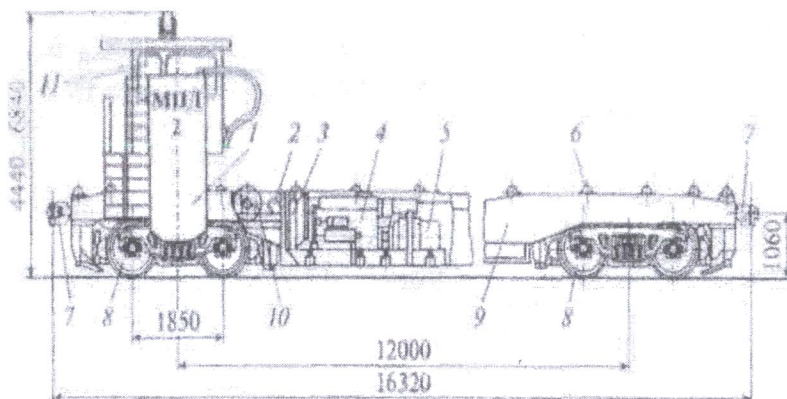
Моторная платформа МПД-2: 1 - порталная стойка с гидроцилиндрами вертикального перемещения кабины управления; 2 - компрессор; 3 - радиатор; 4 - дизель; 5 - генератор постоянного тока; 6 - роликовый транспортер для перетяжки пакетов звеньев; 7 - автосцелка с поглощающим аппаратом; 8 - ходовая тележка с приводными колесными парами; 9 - рама; 10 - лебедка для перетягивания пакетов; 11 - кабина управления
